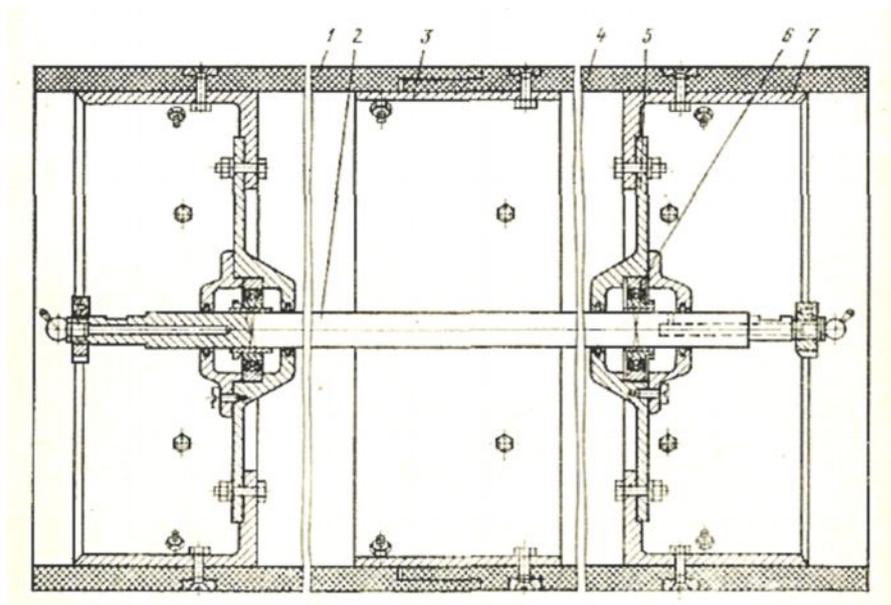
Укатывающий валик: 1- левая половина обечайки, 2- ось, 3- соединительное кольцо, 4- правая половина, 5- диски, 6- шариковые подшипники, 7- чугунные ободы.
